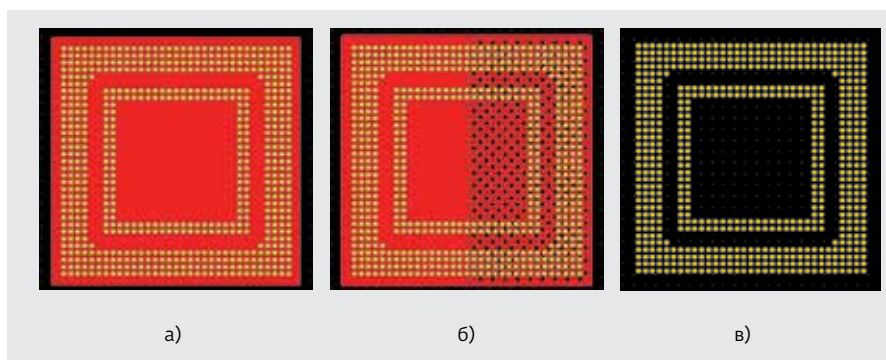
Перекрытие контактных площадок микросхемы сплошными полигонами на тестовой плате: а – полностью; б – на 50%; в – без перекрытия
